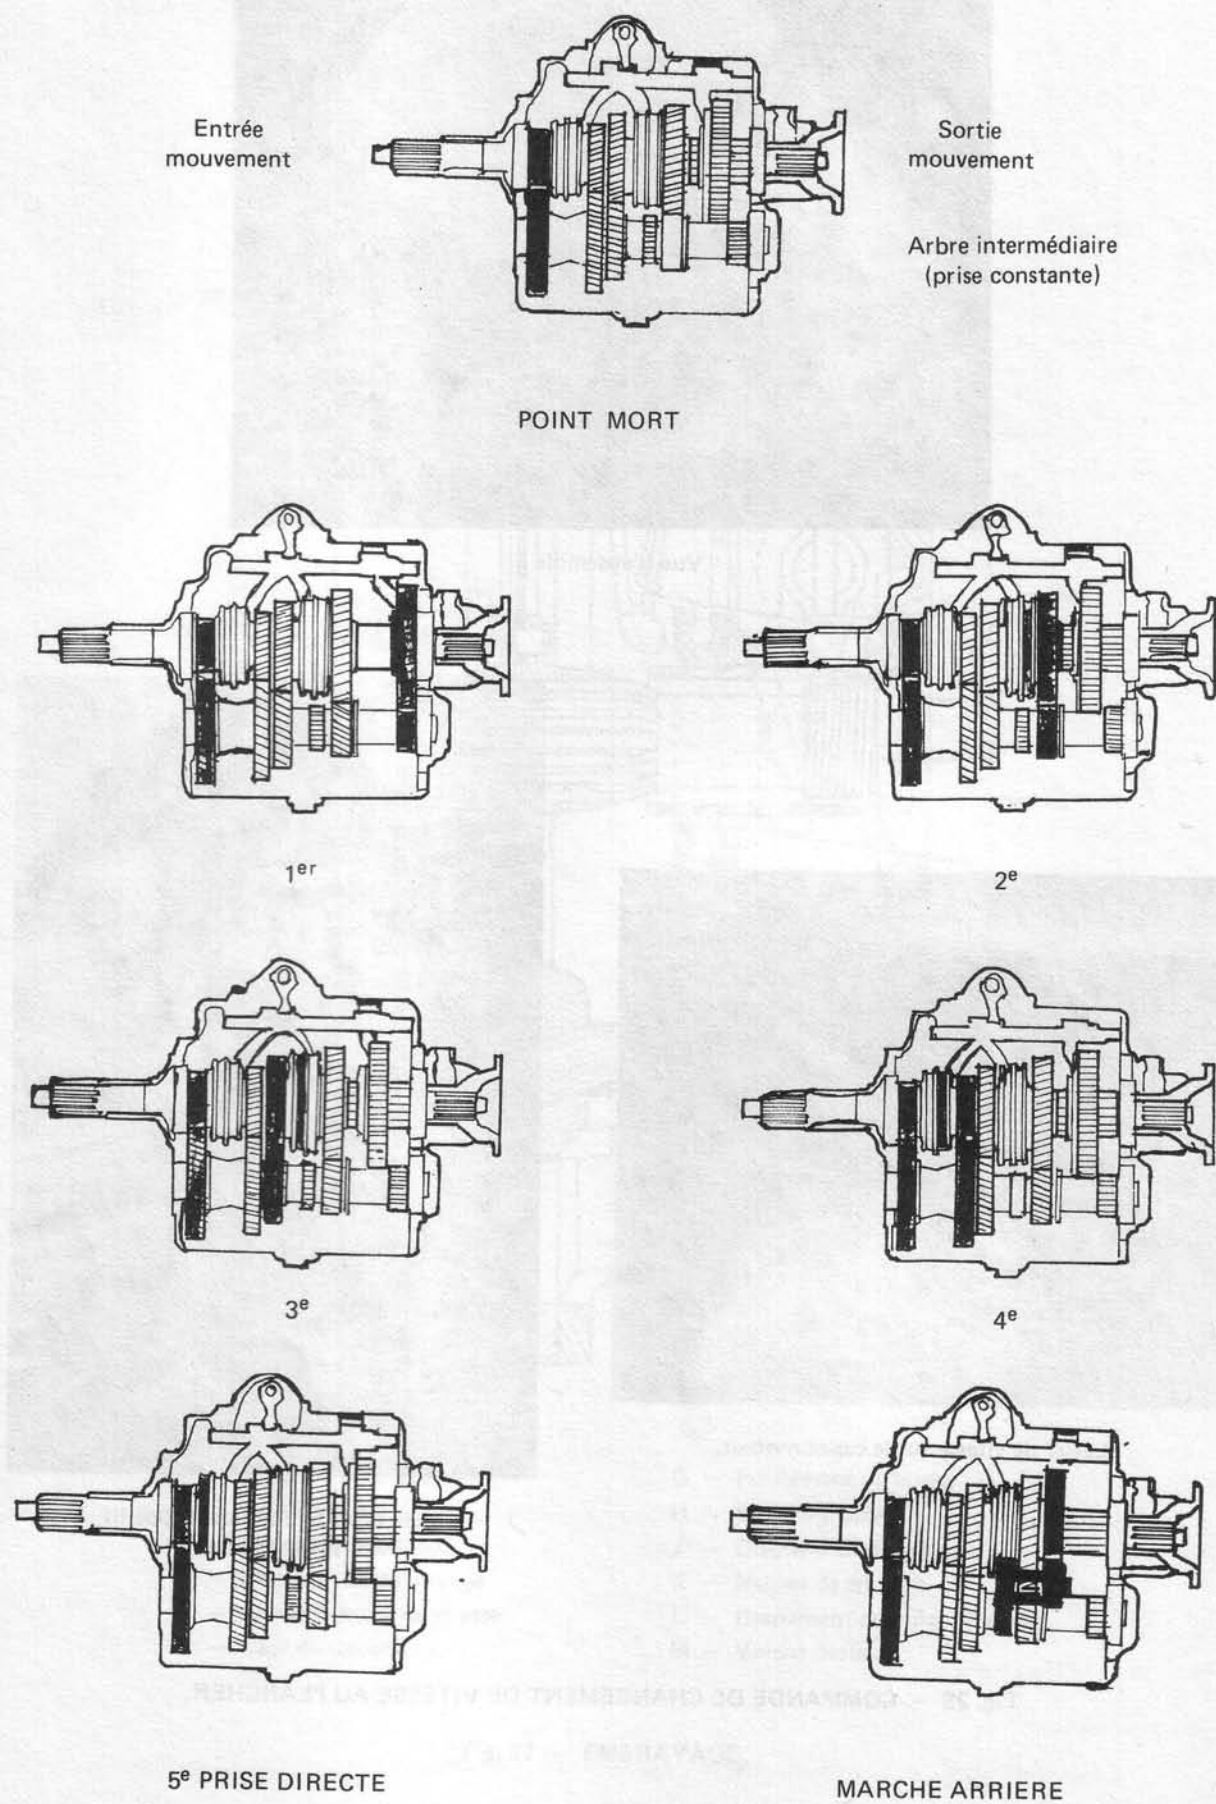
CINEMATIQUE DE LA BOITE DE VITESSE.
